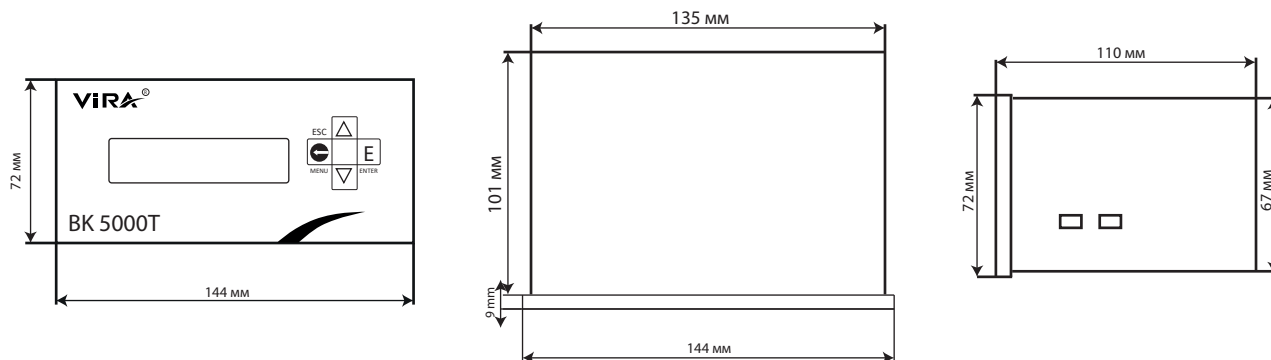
Габаритные размеры корпуса контроллера BK 5000-T
